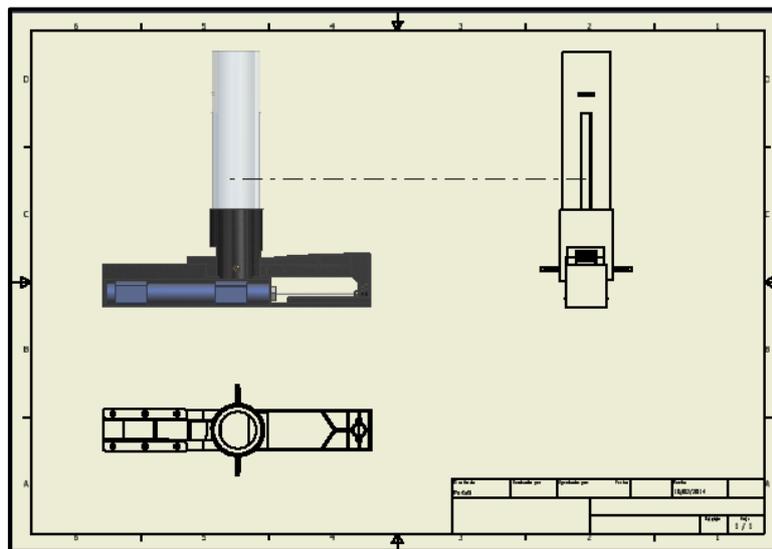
Alzado, planta y perfil del bloque del pistón
